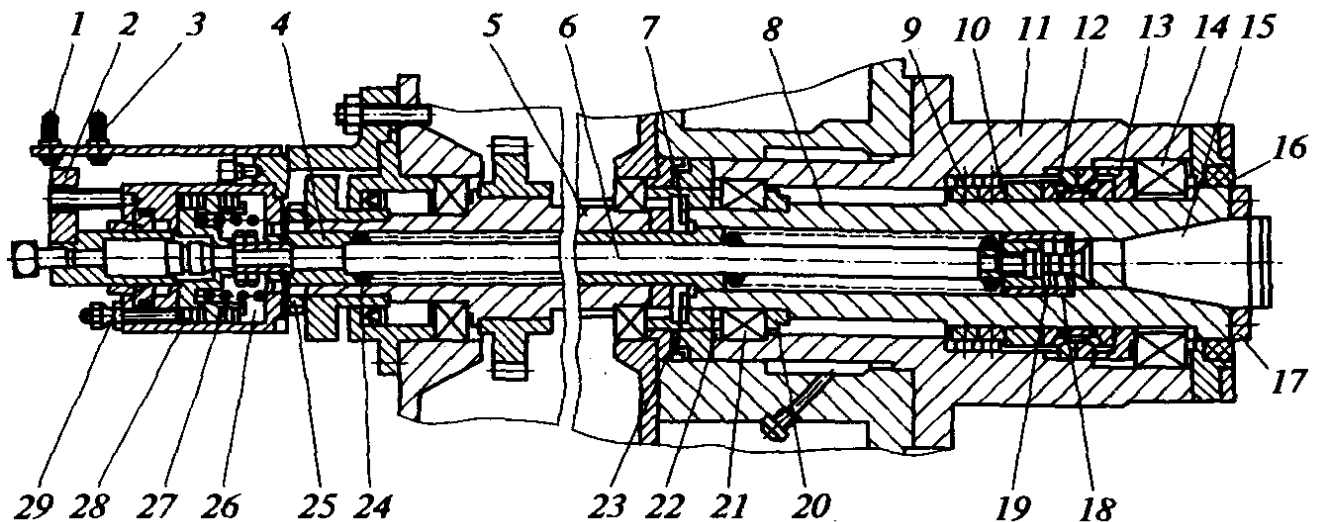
Шпиндельний вузол із механізмом затиску інструменту
